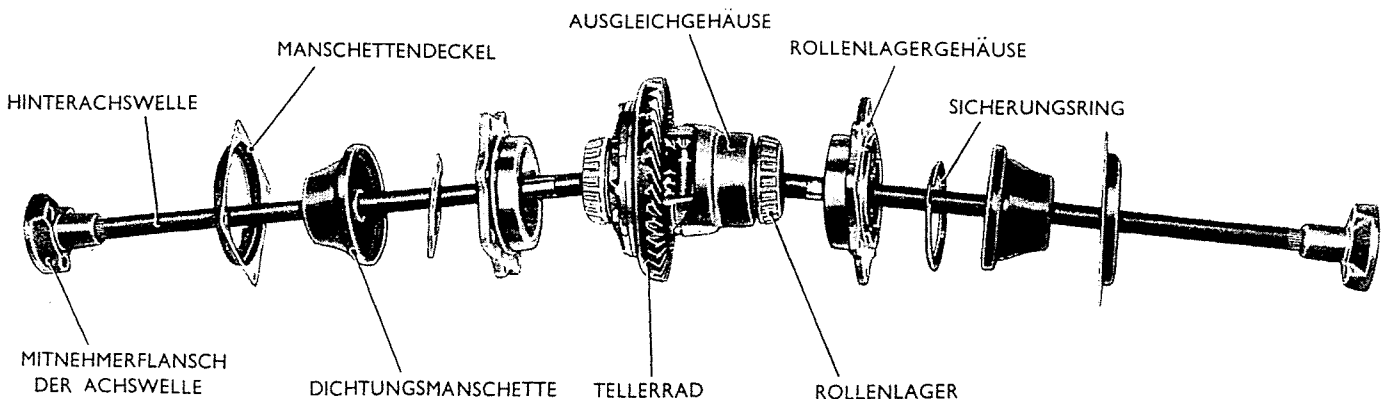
Ausgleichgetriebe komplett mit den Hinterachswellen.
